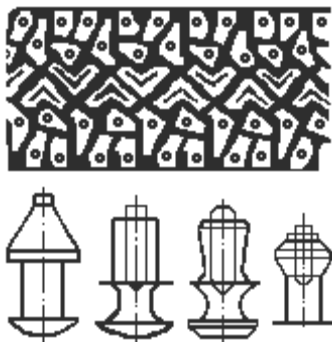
Шини з шипами проти ковзання та шипи
